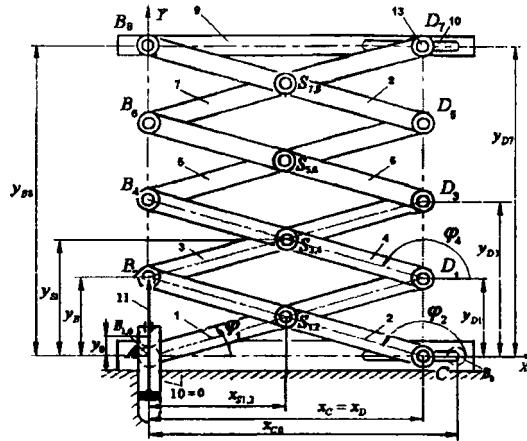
Кинематическая схема рычажного механизма ножничного подъемника
